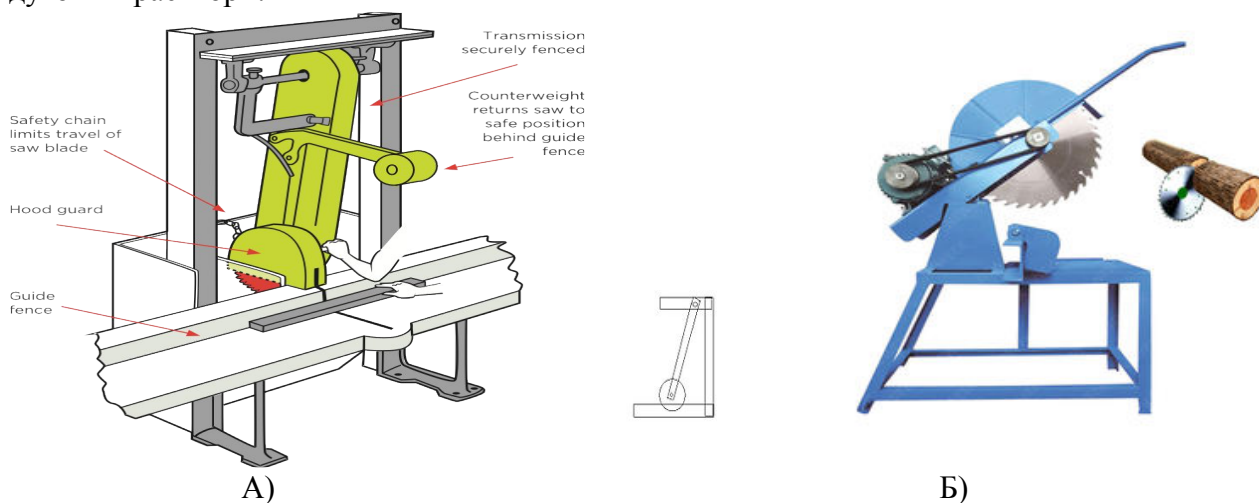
Торцювальний маятниковий (А) та балансірний (Б) верстат.
